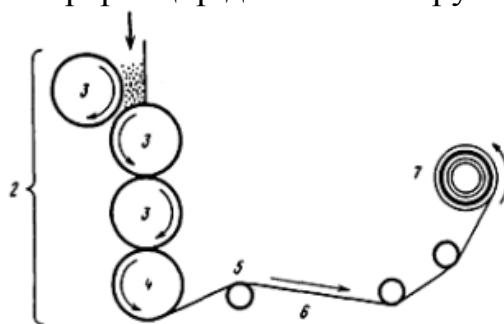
Схема апарату для каландрування 1 - полімерна сполука; 2 – каландрувальні валки: гарячий (3) холодний (4); 5 – каландрувальний лист; 6 – валки, що направляють; 7 – змотуючий пристрій
